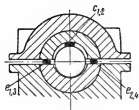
Проверка зазоров между валом и вкладышами подшипника.
